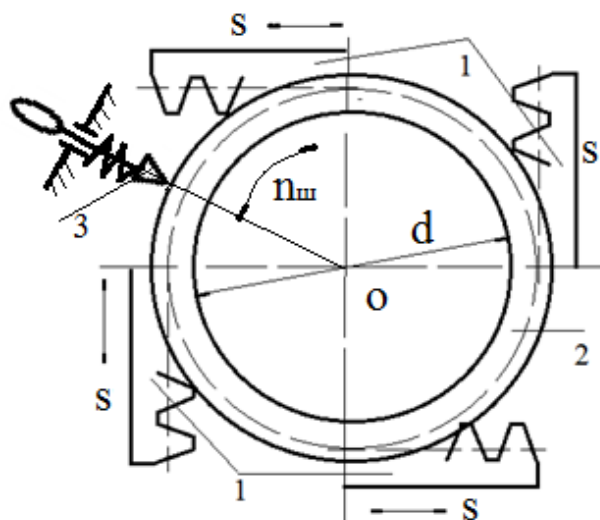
Принципиальная схема разделки кабеля с зубчатым реечным механизмом установки ножей на диаметр: 1 – рейка механизма радиального перемещения ножей, 2 – реечная шестерня, 3 – механизм фиксации шестерни (ножей на диаметр); d – максимальный диаметр разделяемого кабеля, i_c – передаточное отношение редуктора, s – радиальное перемещение ножа, n – частота вращения ножа, $n_{ш}$ – поворот реечной шестерни.
